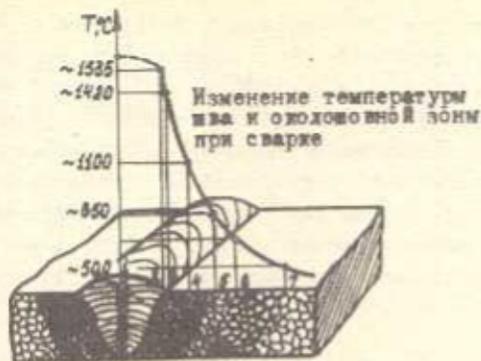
Структура металла шва и околошовной зоны после сварки плавлением
